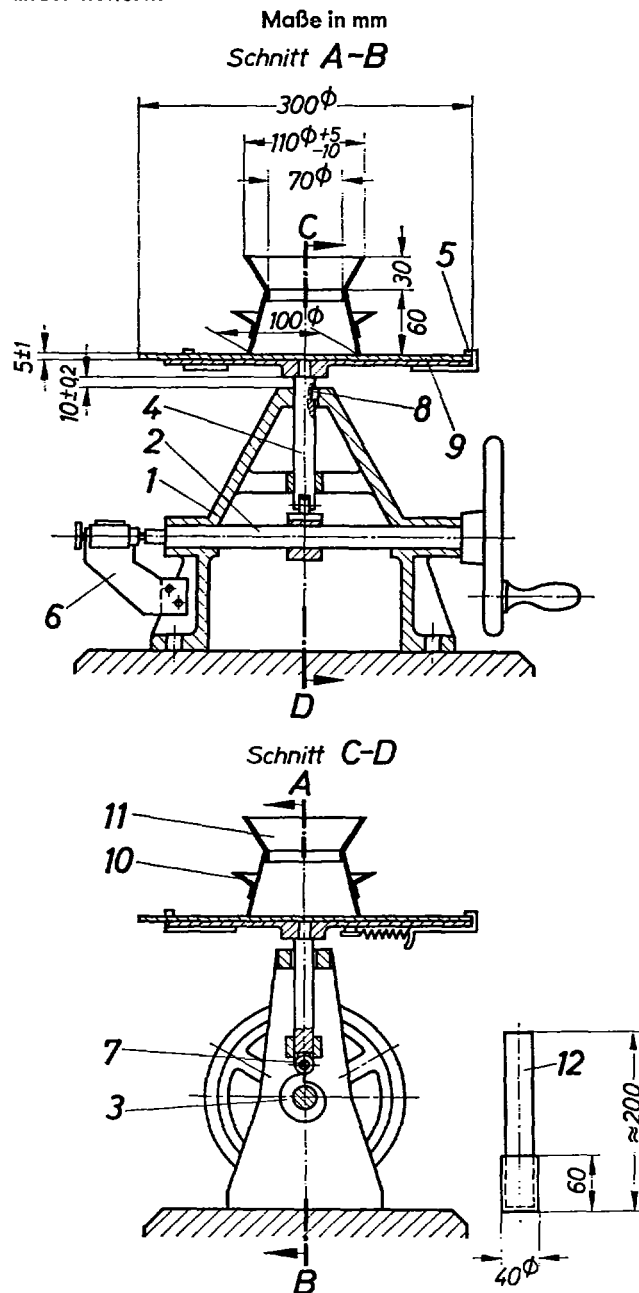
Ausbreitisch und zugehöriger Stampfer (Bild rechts)
